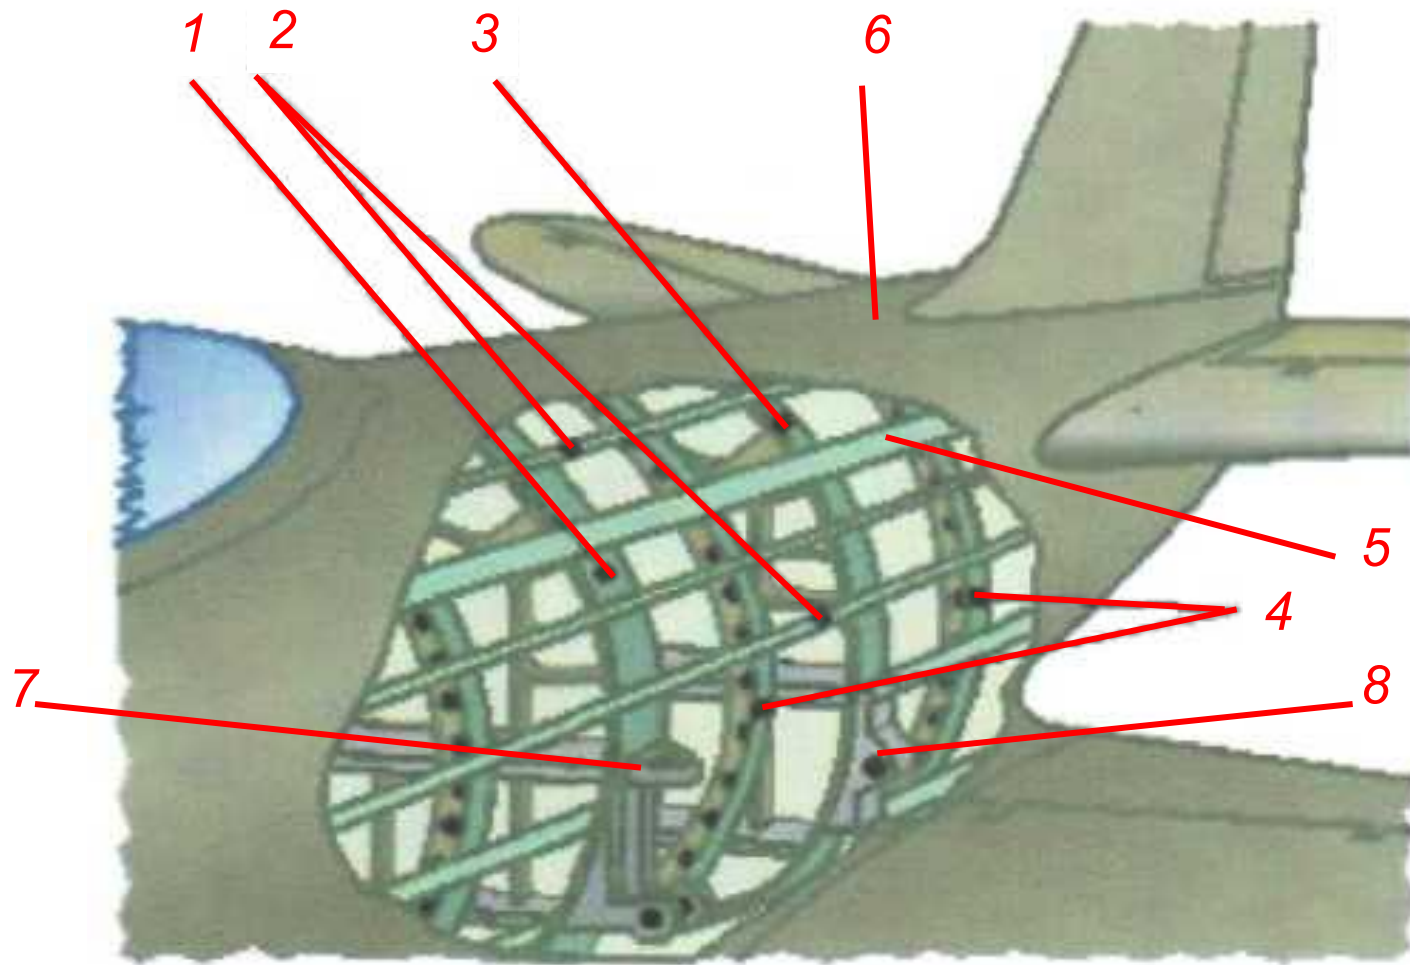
Элементы конструкции лонжеронно-балочного фюзеляжа: 1, 3 - усиленный шпангоут; 2 - стрингер; 4 - нормальный шпангоут; 5 - лонжерон, 6 - обшивка; 7 - моментный узел; 8 - шарнирный узел.
